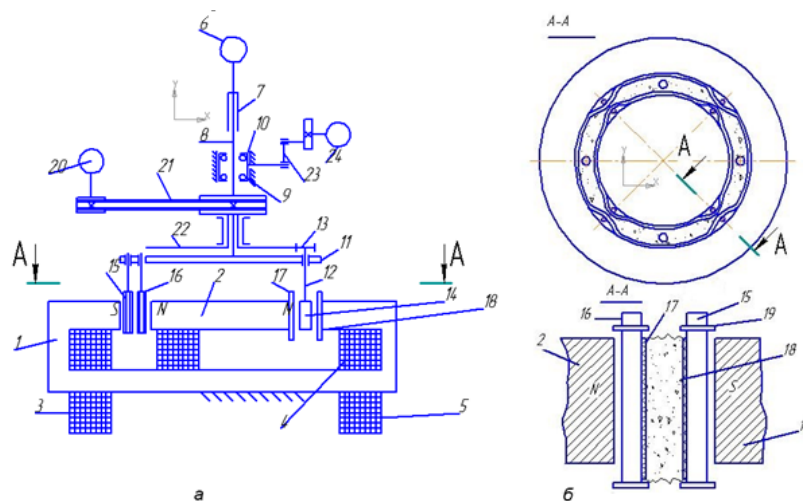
Схема установки для MAO поверхностей малогабаритных деталей машин:
